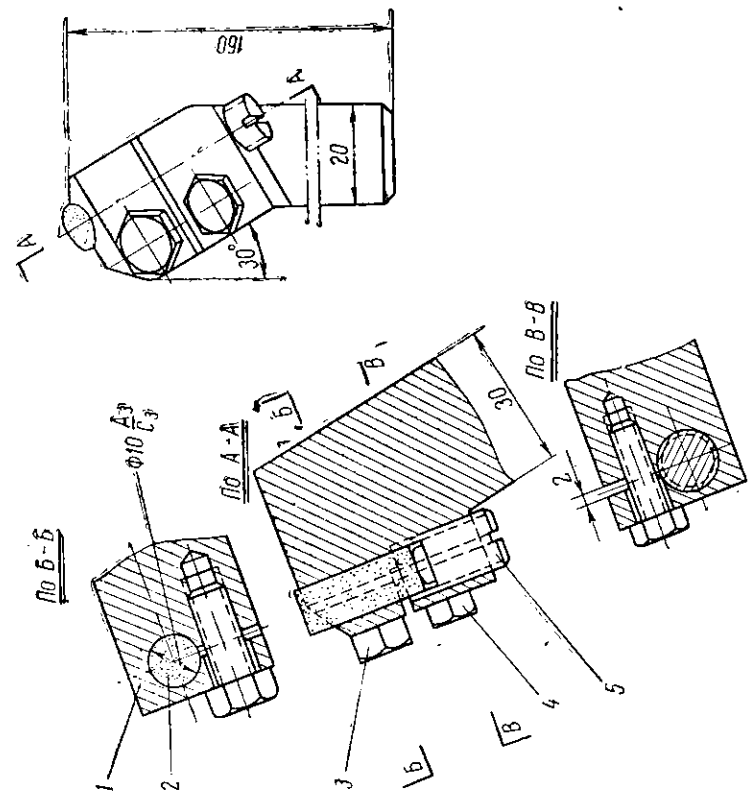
Резец для расточки подшипниковых колец на станках МР5 (завод им. Куйбышева).
